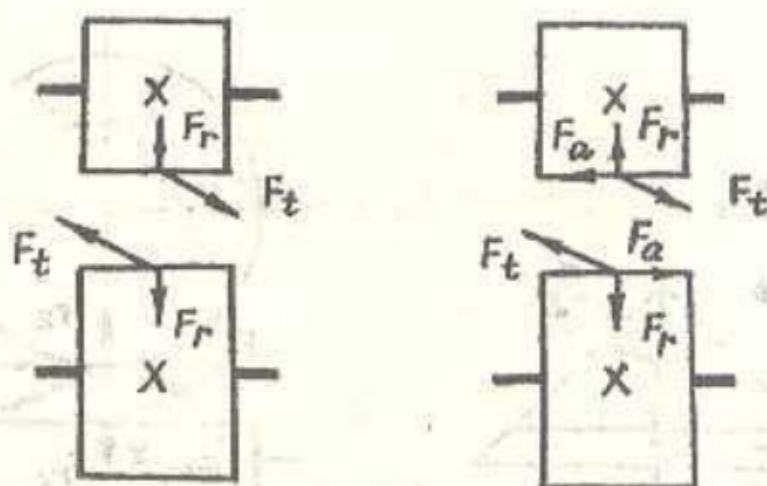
Силы в зацеплении цилиндрических зубчатых колес: а) прямозубых; б) косозубых
